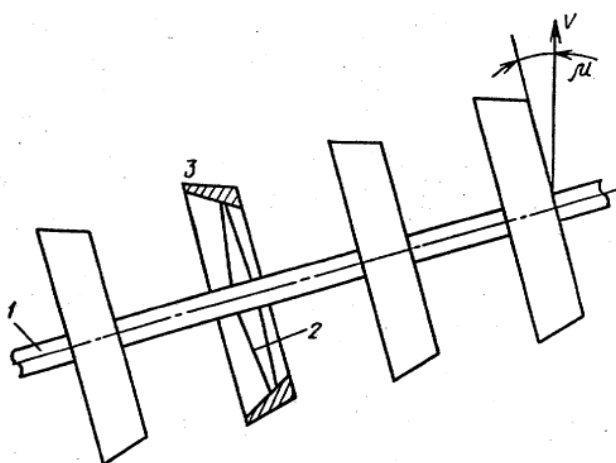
Грунтоуплотняющий каток с конусными элементами рабочей поверхности (А.с. 1496650)
